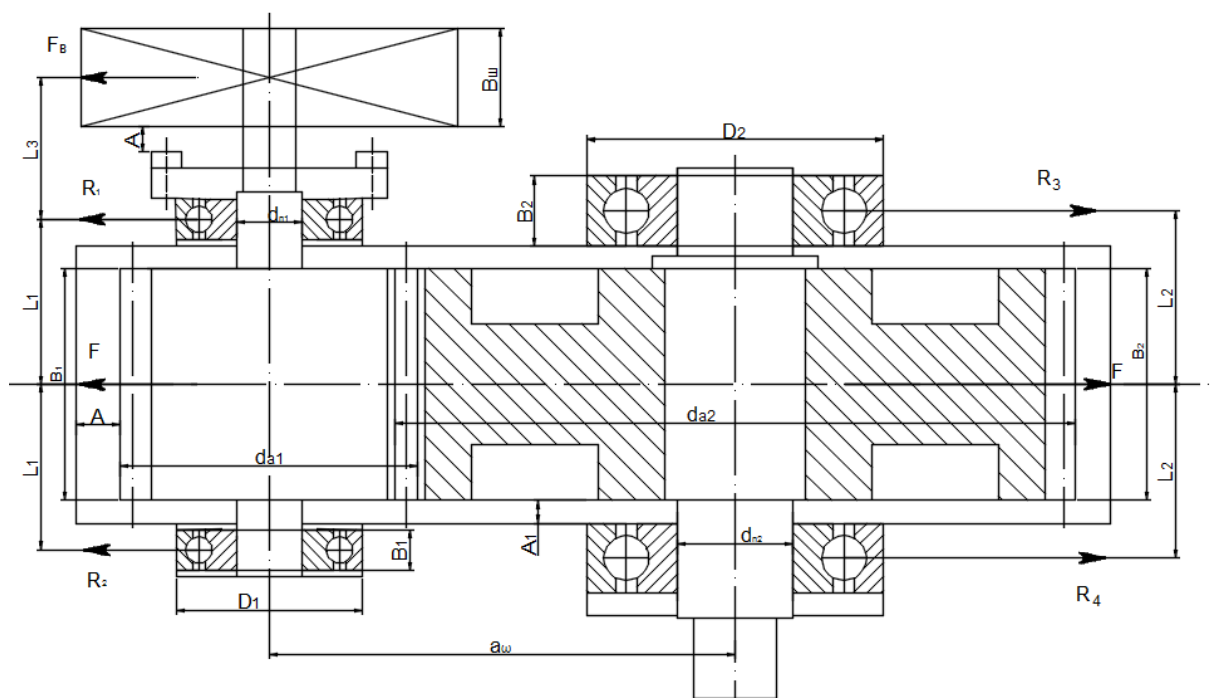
Эскизная компоновка цилиндрического редуктора
